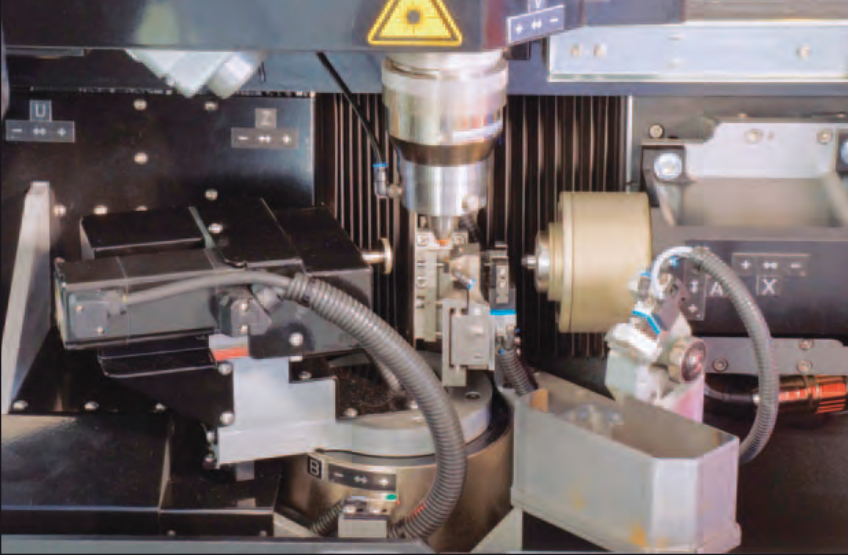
Die Konifiziereinheit wird mechanisch eingeschwenkt, die Spitzengeometrie oder die Form der Mantelfläche umgeformt, ein Schweißpunkt auf die Spitzengeometrie gesetzt und die Spitzengeometrie mit diamantbeschichtetem Schleifwerkzeug überschleift. Das integrierte Entnahme-Handlingsystem entnimmt das fertige Teil aus dem Arbeitsbereich und legt es in einem Behälter ab
